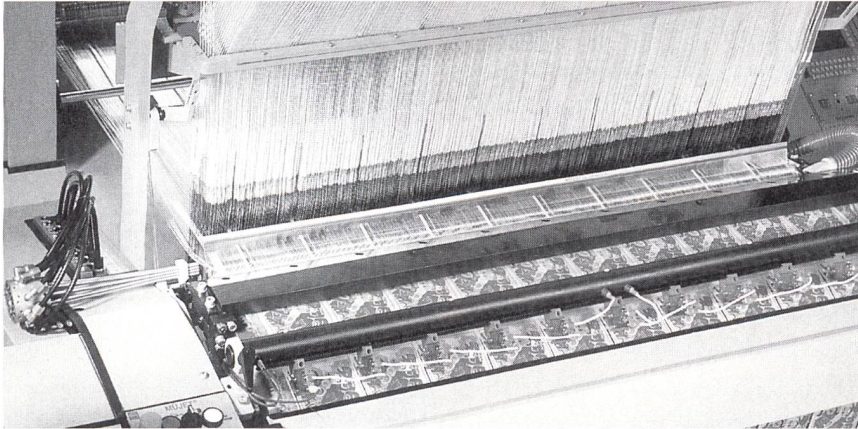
Die Luftdüsenwebmaschine MÜJET für Etiketten
